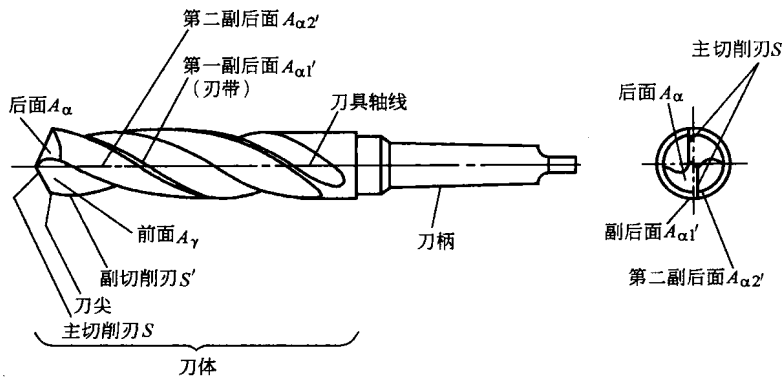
麻花钻切削部分上的切削刃和刀具表面
